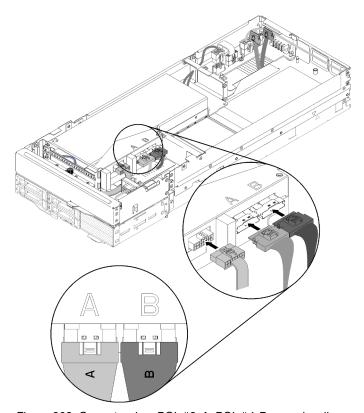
Conectando o PCIe#3-A, PCIe#4-B e o cabo diverso da placa riser ao conjunto da placa riser frontal.
